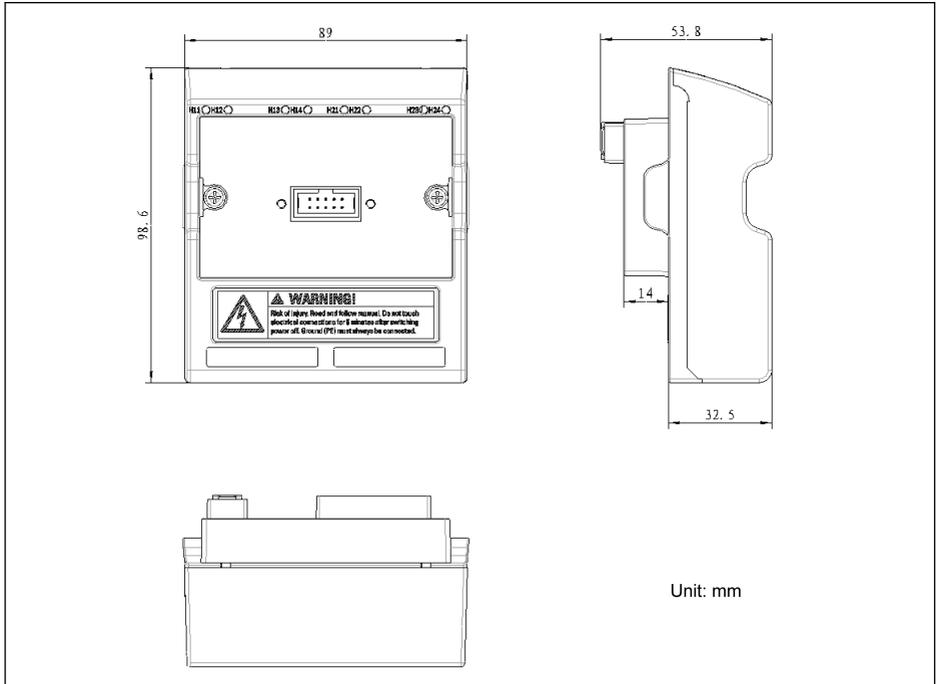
Dimensiones del módulo de tarjeta de extensió
